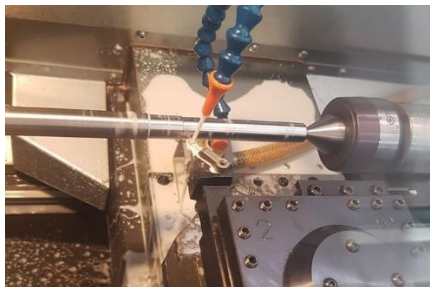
Maquinado de eje principal en Torno CNC HAAS.
